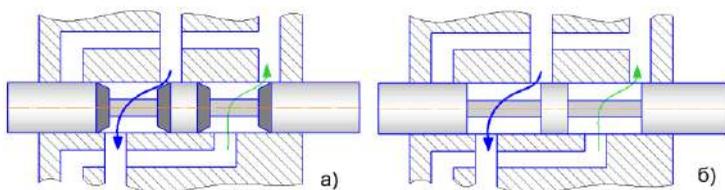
Пояски золотника: а – конічні; б – циліндричні
